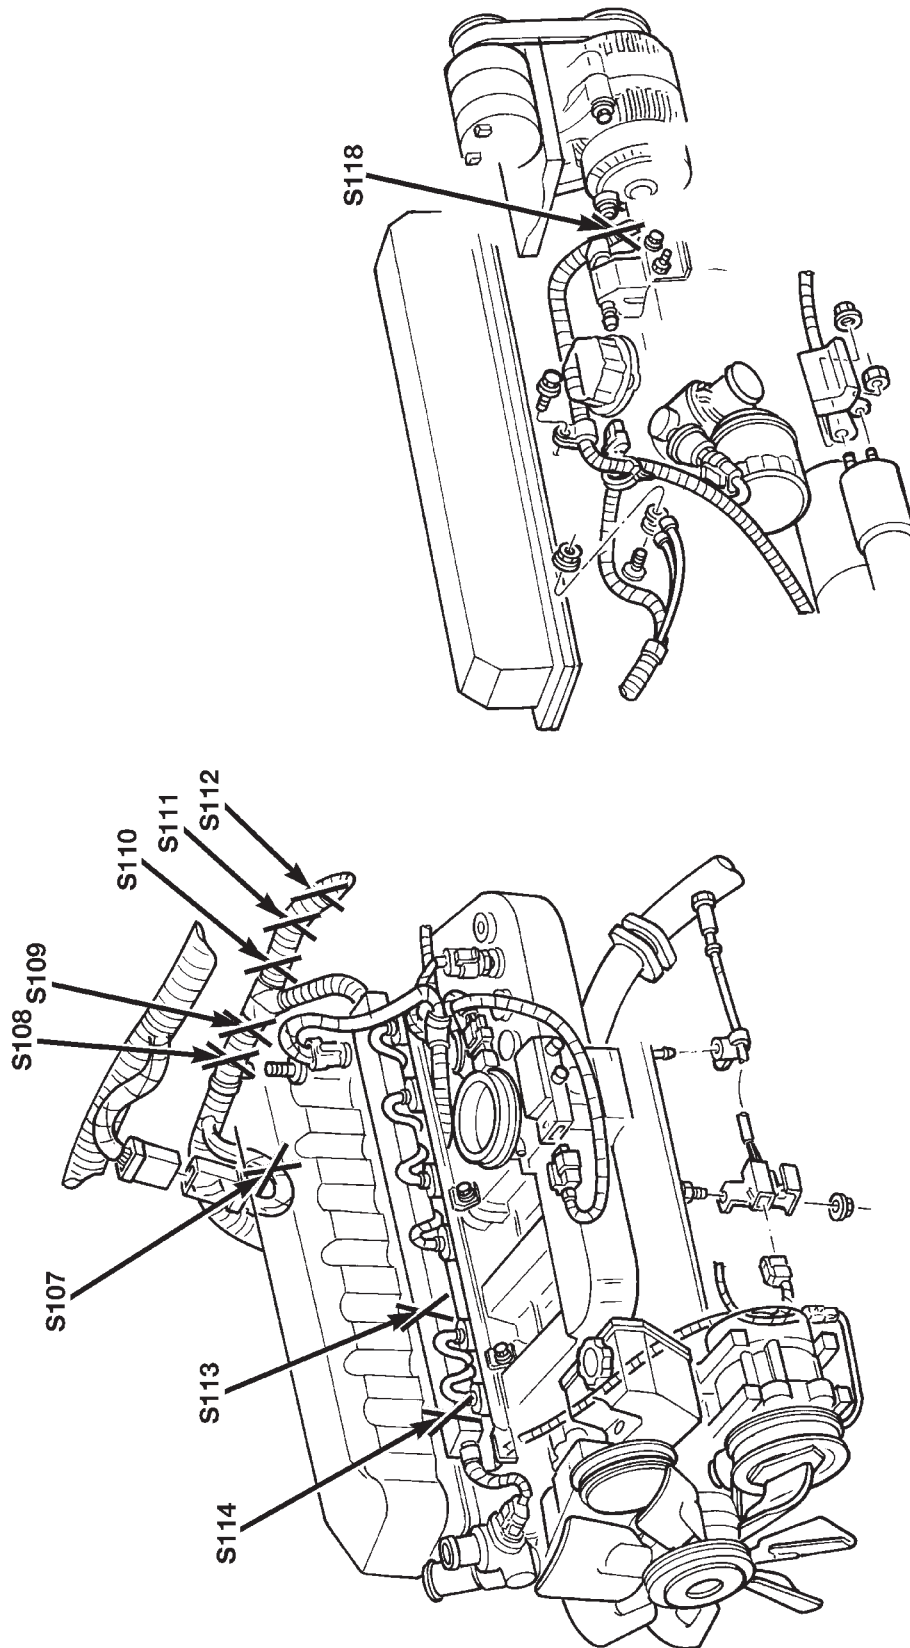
Empalmes de cableado del motor - Motor 4.0L
